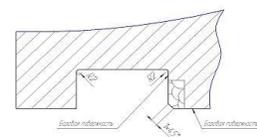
Обработка наплавки расточки ЦВД под обойму КУ № 1
